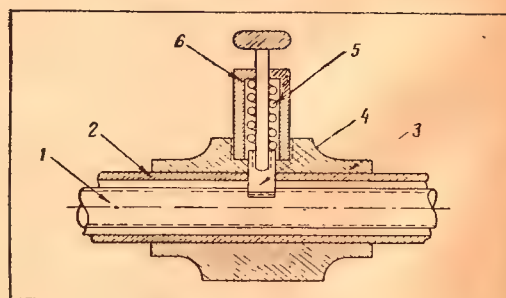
Устройство смещения с трубчатой направляющей; ходовой винт находится внутри направляющей. 1 — ходовой винт; 2 — направляющая; 3 — ползун; 4 — зубчатая гребенка; 5 — пружина гребенки; 6 — обойма пружины
